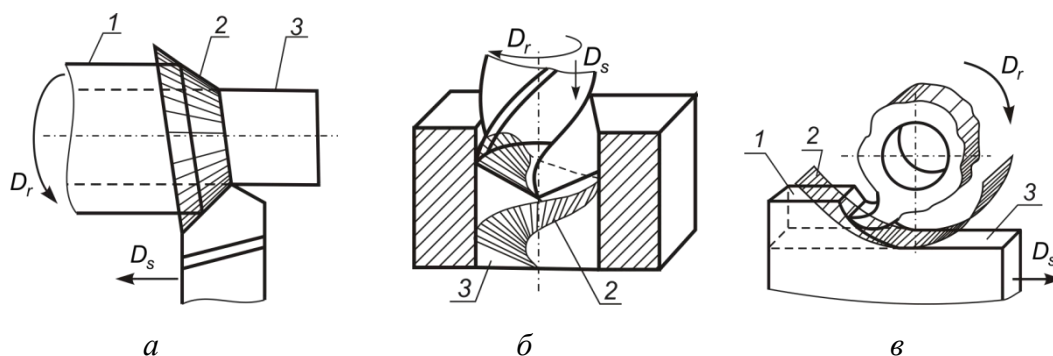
Поверхности при точении (а), сверлении (б) и цилиндрическом фрезеровании (в):
